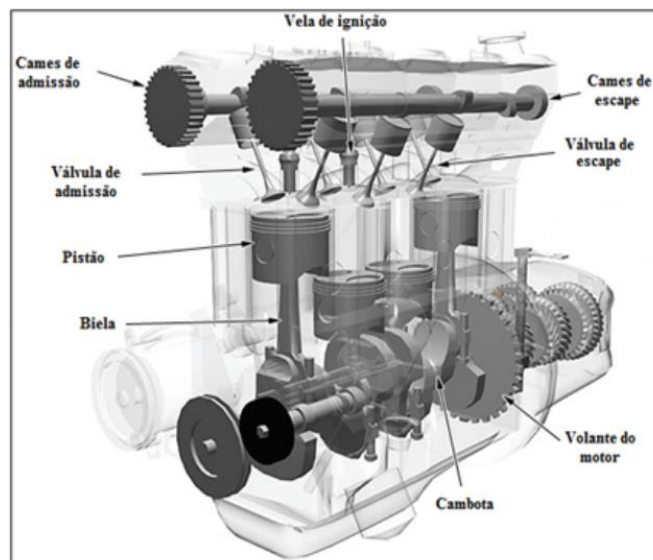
Vista de um motor de combustão interna e seus principais componentes [46]
